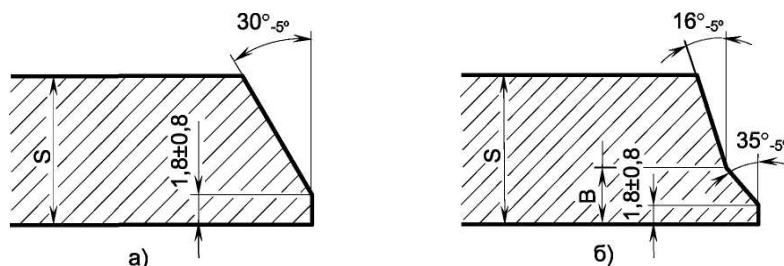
Форма разделки кромок труб для комбинированной сварки с применением Комплекса автоматической сварки
